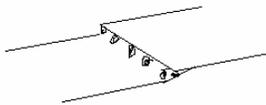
Soldadura por puntos de difícil acceso para las operaciones de limpieza superficial.
